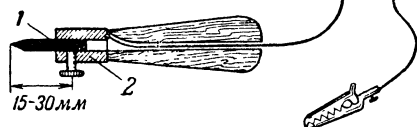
Сварочный аппарат для сварки проводов.
